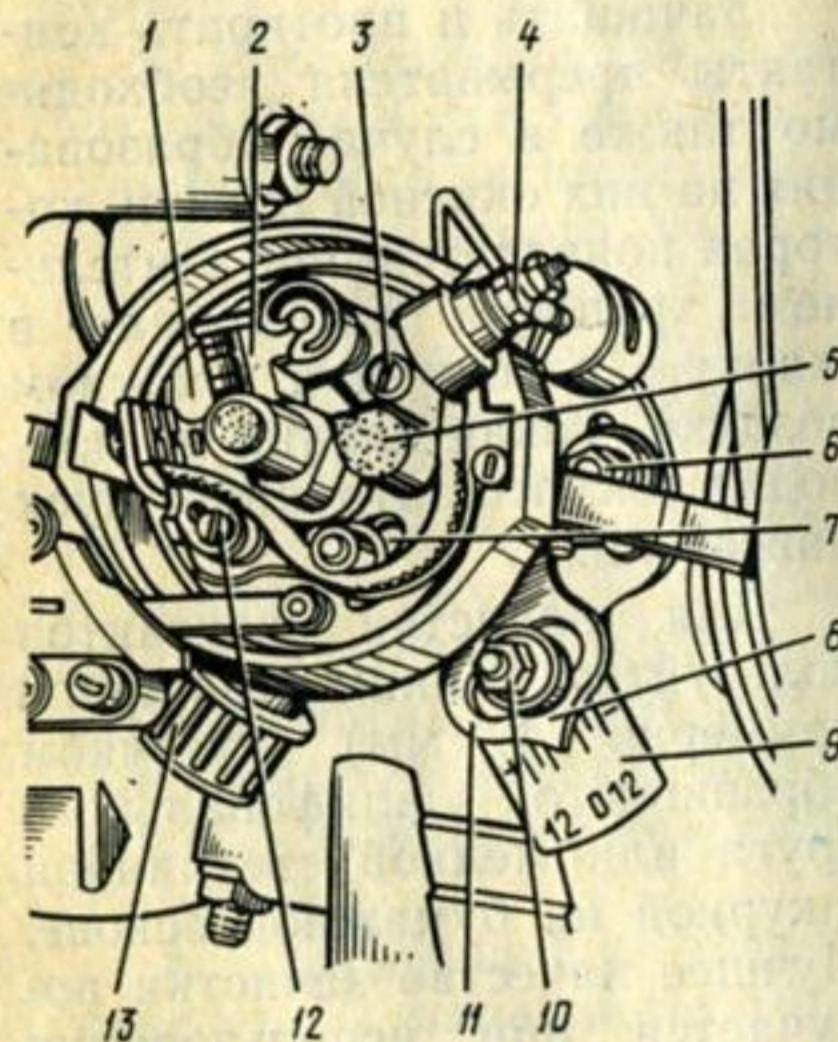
Распределитель зажигания (со снятыми крышкой и ротором):
